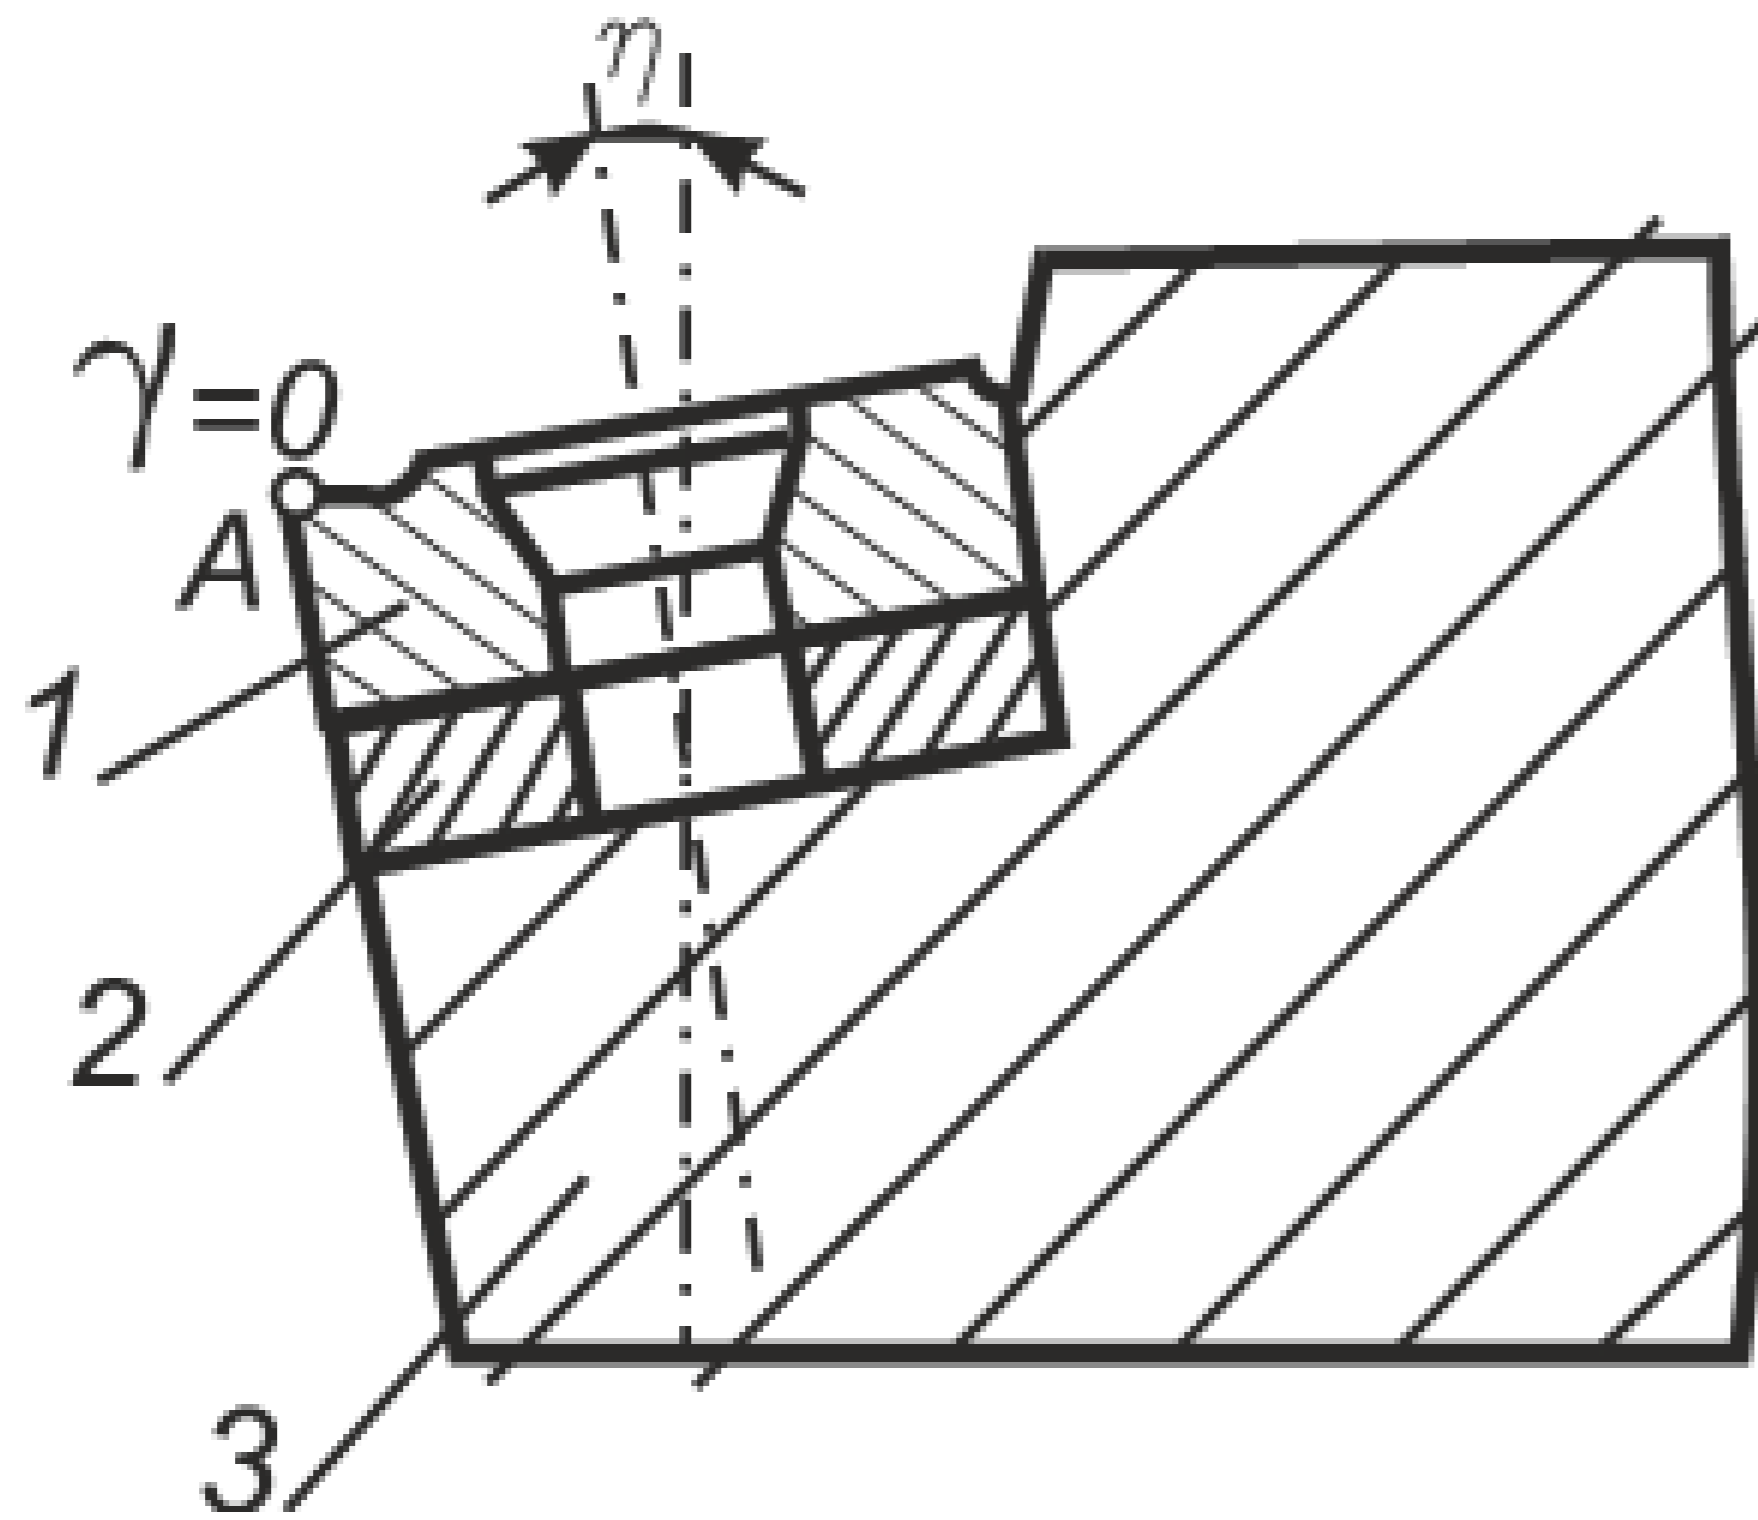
Схема установки пластины на рабочей части резца при которой передний угол в вершинной точке А стає рівний нулю. Цифрами позначено:
